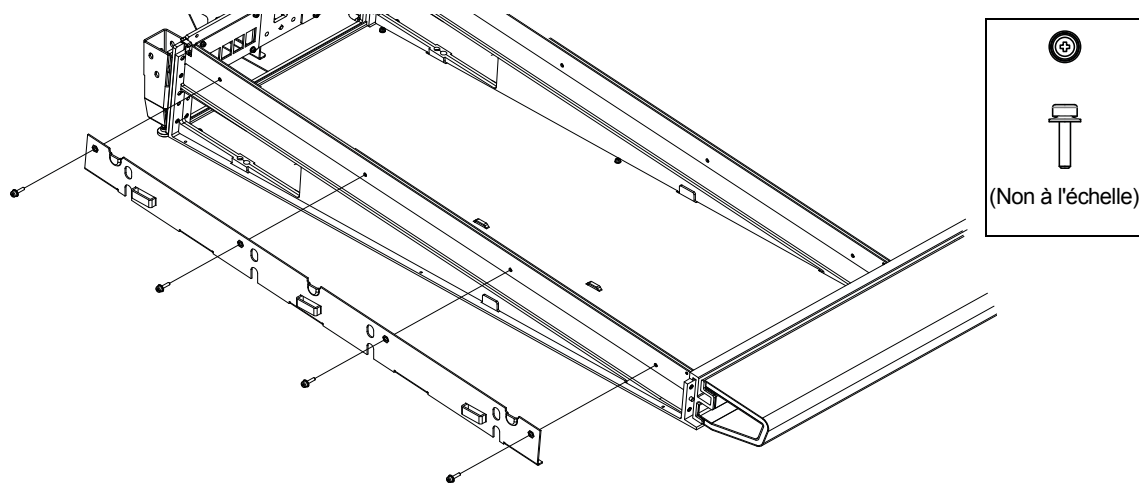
Fixation de la plaque de montage du panneau latéral gauche
